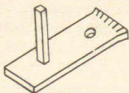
Ножка верстака      Рис. 5. Подвижная часть бокового винта
